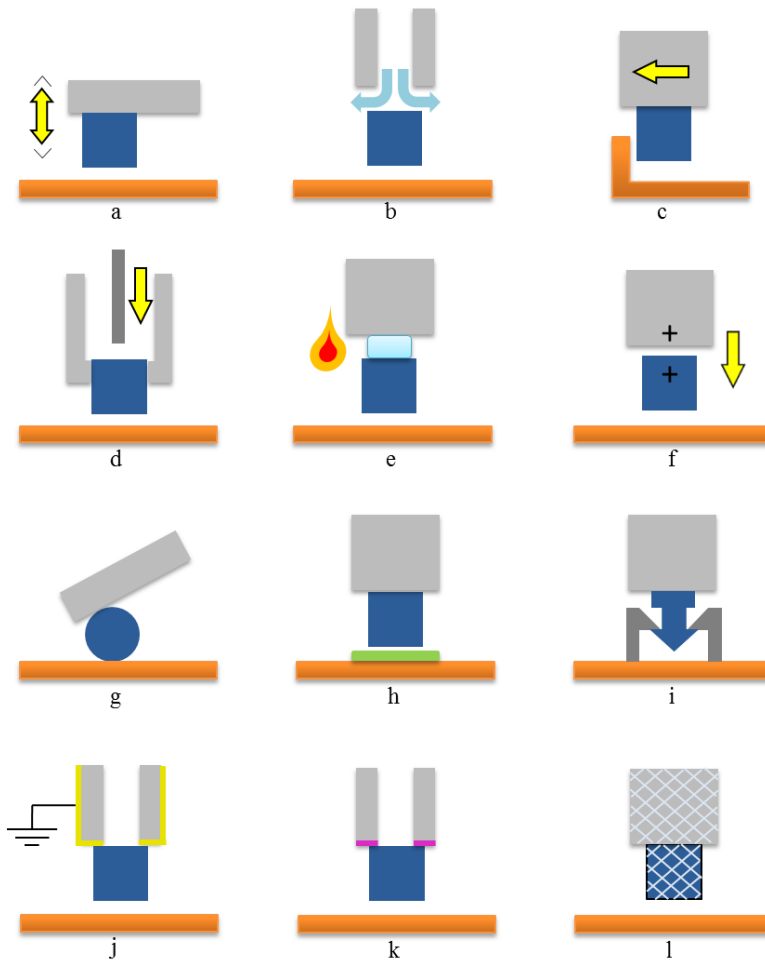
Freigabestrategien: (a) Schwingung; (b) Druckimpuls; (c) Kante; (d) zusätzliches Werkzeug; (e) Verschwinden des Mediums; (f) elektrische Abstoßung; (g) Rollen; (h) Kleben; (i) mechanisches Einrasten; (j) Beschichtung; (k) hydrophobe Beschichtung; (l) gleiches Material.
